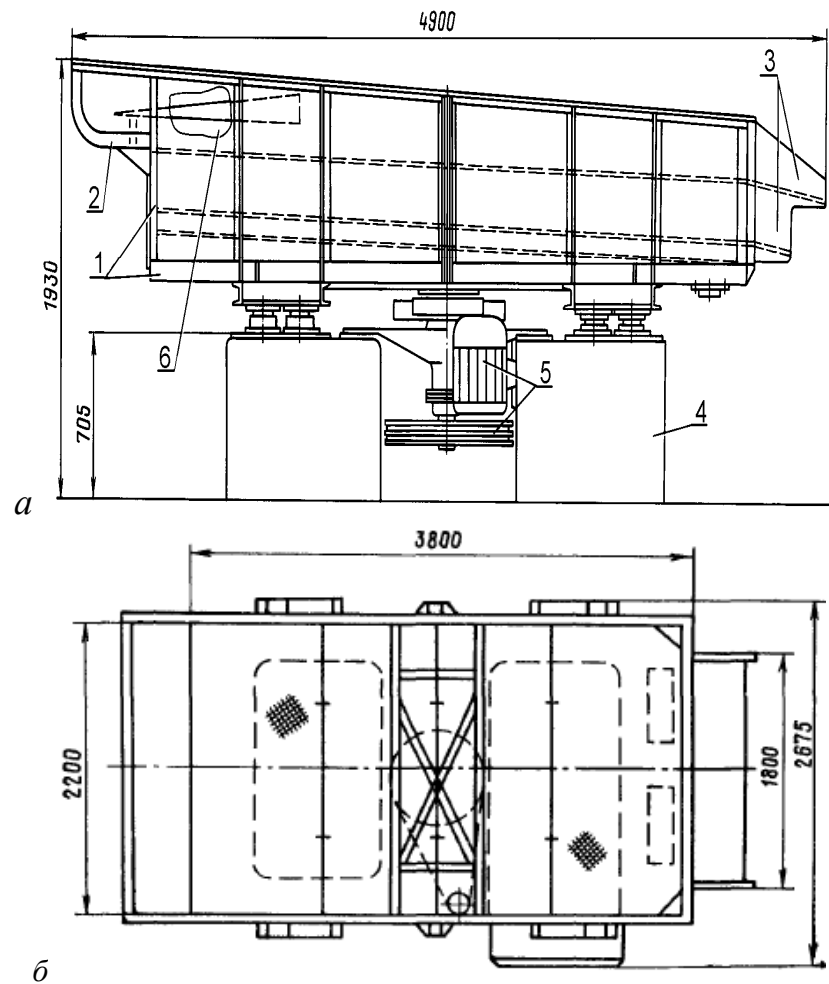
Сортировка щепы плоская СЩ-120 (а) вид сбоку; б) вид сверху) [22]:
